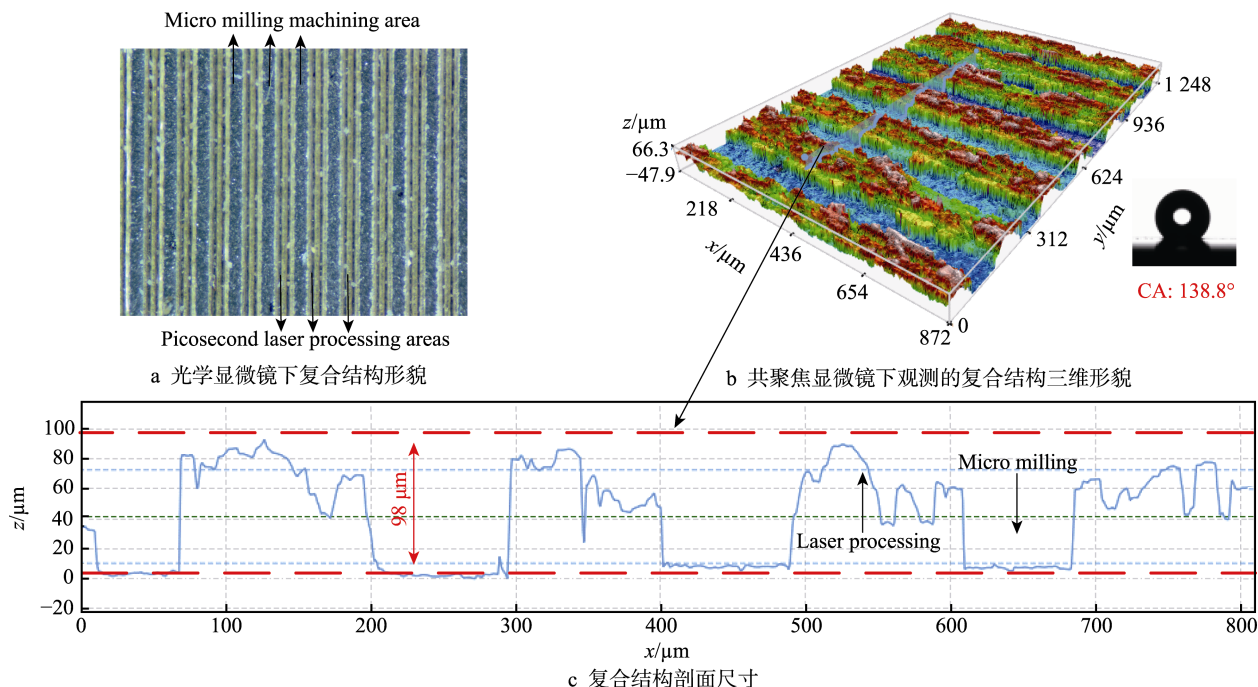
0.1 mm 微槽复合结构的表面形貌及尺寸
